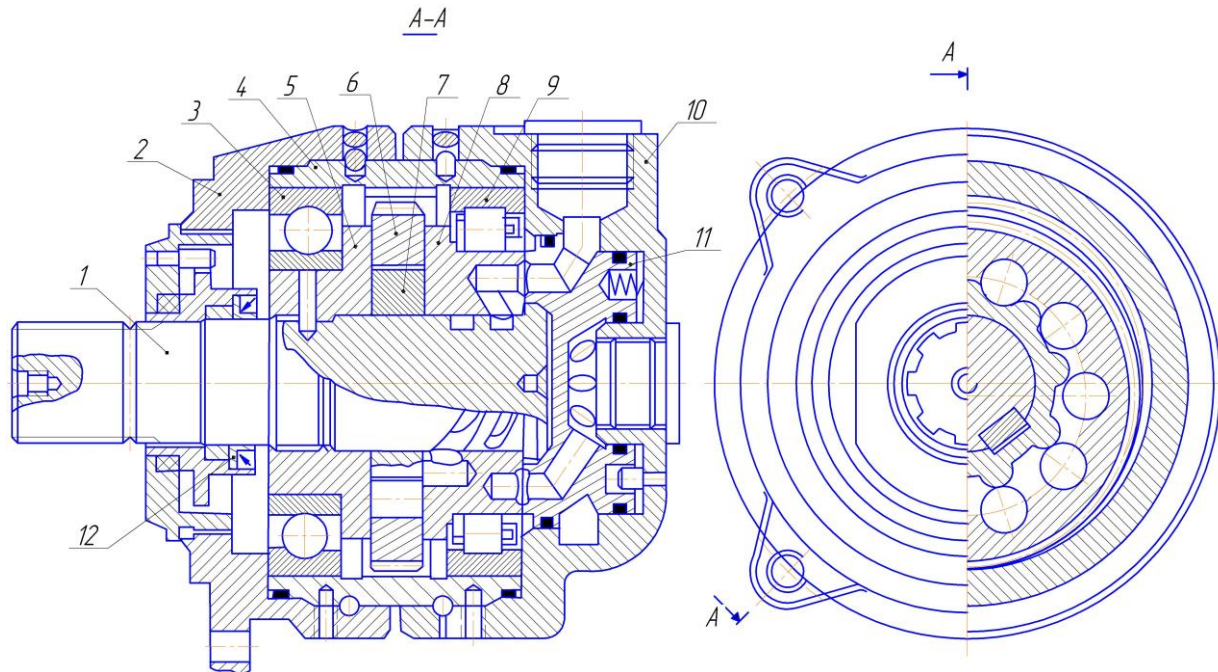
Планетарний гидромотор серії ГПР-Ф: 1 – вал; 2 – передня крышка; 3 – подшипник радіально-упорний; 4 – корпус; 5 – щека; 6 – охоплюючий витеснитель (ротор); 7 – охоплюваний витеснитель (шестерня); 8 – розподільник; 9 – подшипник роликів радіальний; 10 – задня крышка; 11 – золотник; 12 – ущільнювальний вузол.
